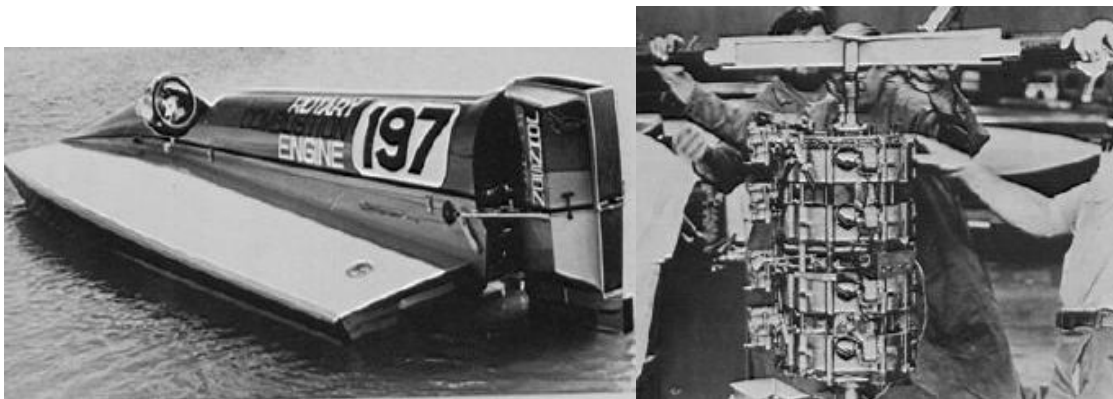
y 70.- Lancha de competición clase open equipada con motor rotativo Wankel fabricado por Johnson. Mecánicos ajustando piezas del motor.
